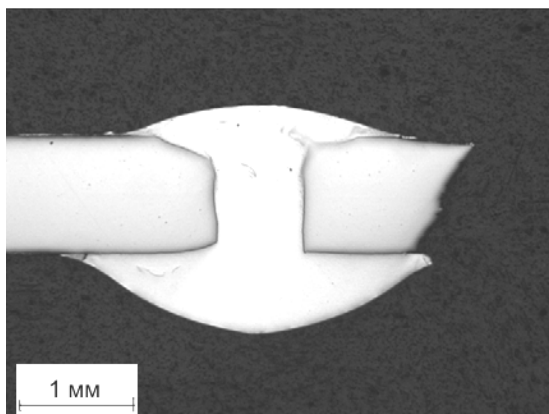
Разрушение паяного образца 22MnB5 и стали DP980 в области DP980
